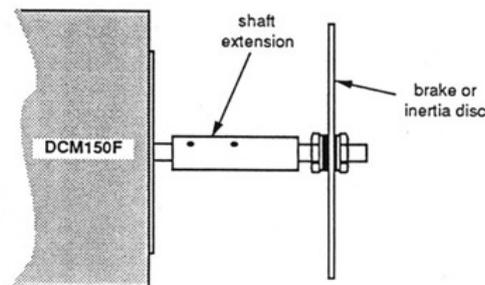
Detalhe do acoplamento do freio magnético ao módulo motor DCM150F.
